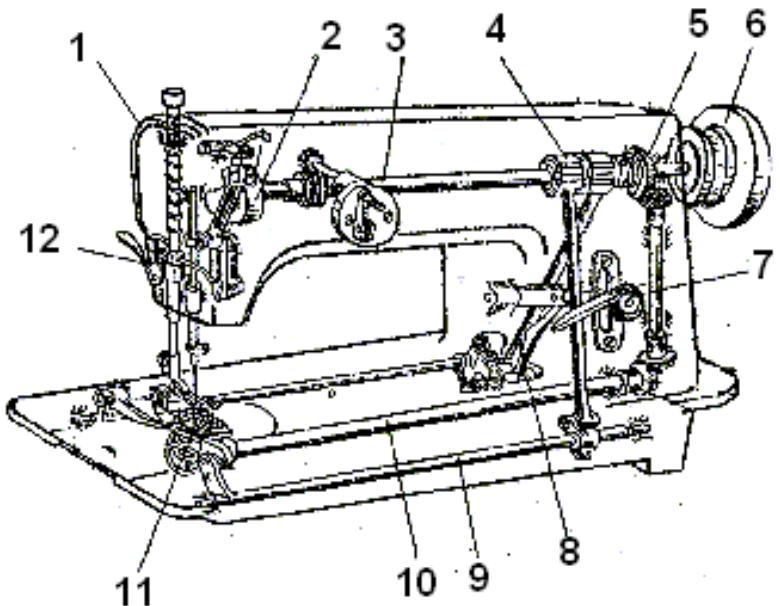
Конструктивная схема головки походной машины 322-М класса:
